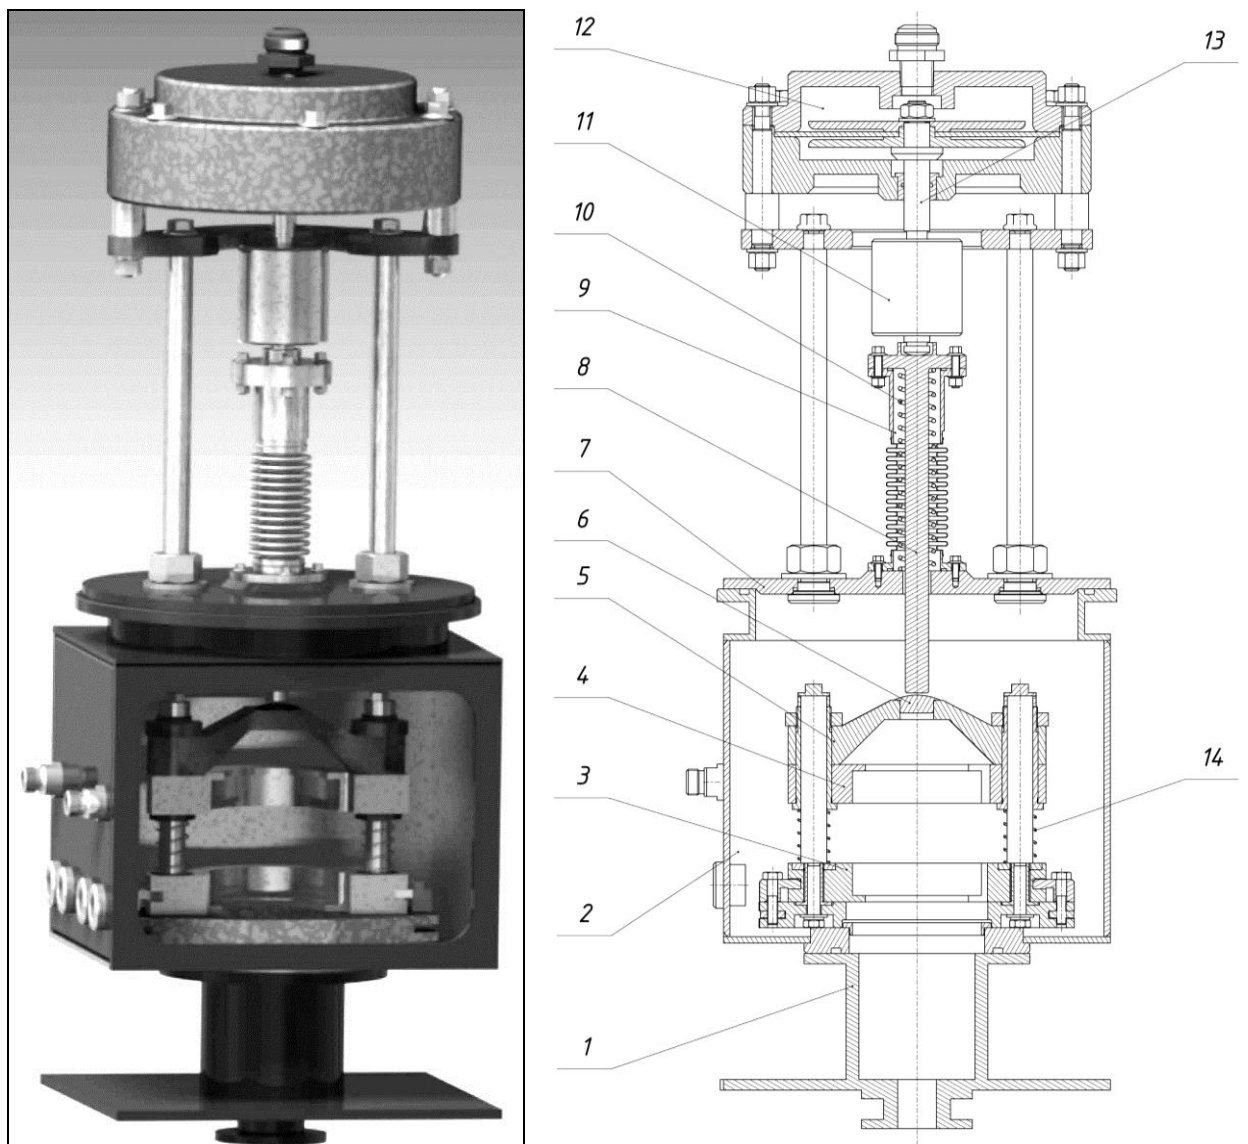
Внешний вид и вертикальный разрез сварочного модуля
